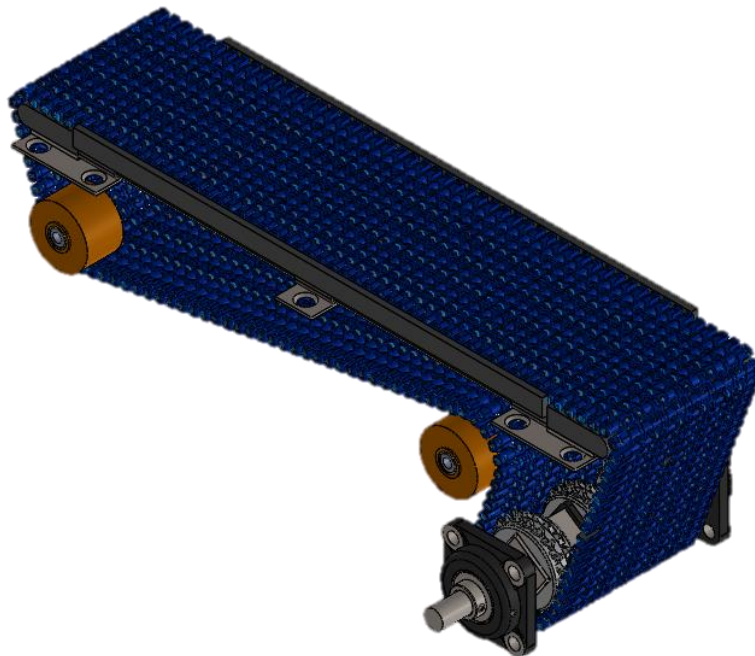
Dibujo CAD que muestra la directriz de diseño con sus componentes y elementos de sujeción.
